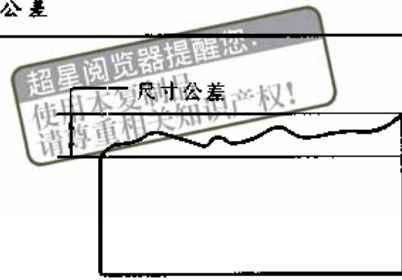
平行度未注公差值等于尺寸公差值
